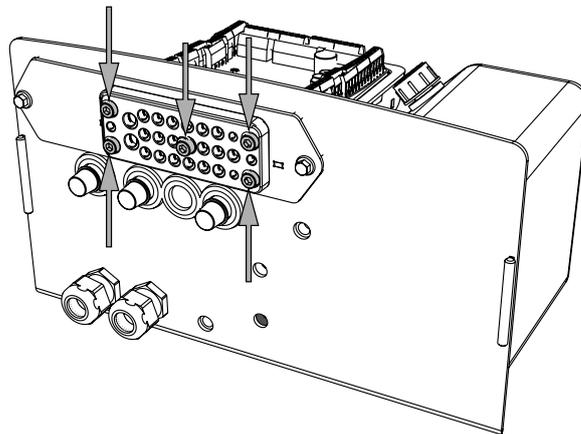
Die fünf Schrauben der Kabeldurchführung
